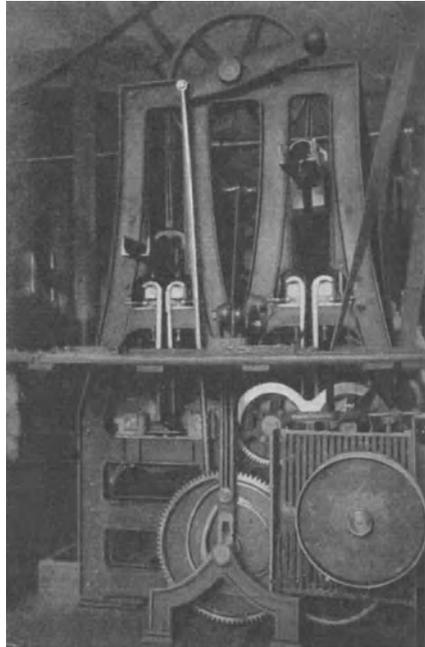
Horners Patent-Stripper-Hechelmaschine.
